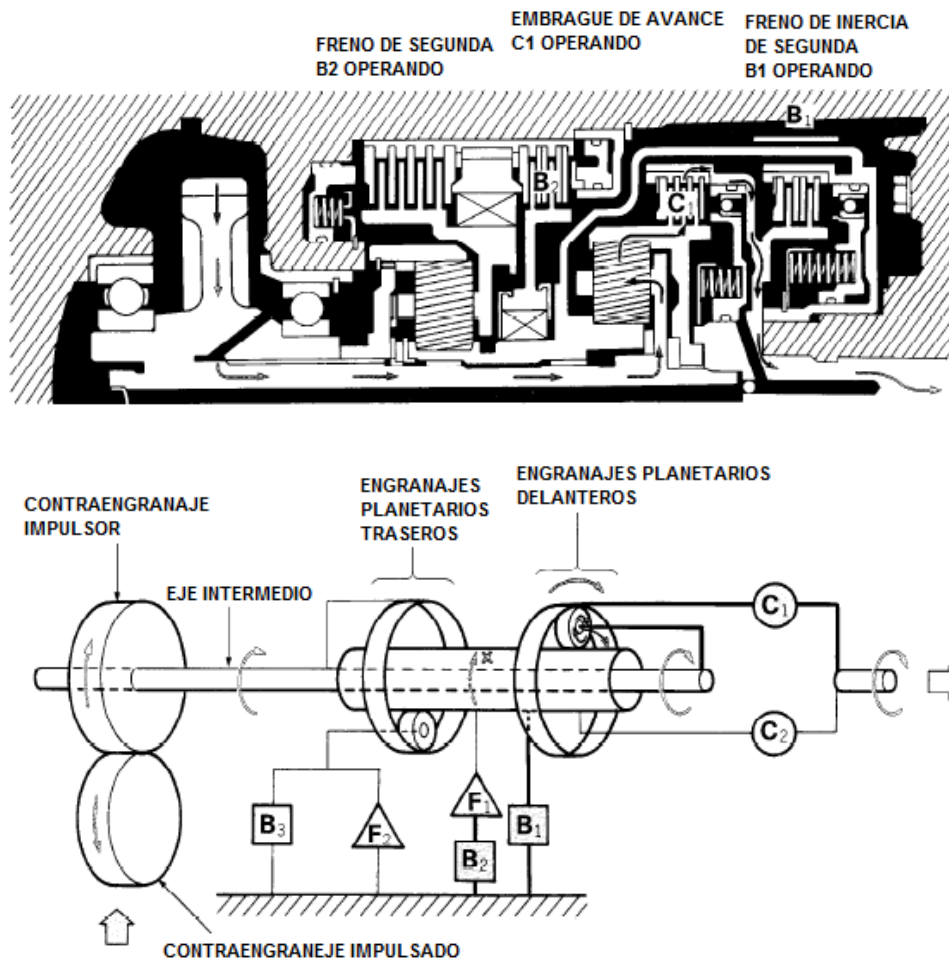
Transmisión en rango “2”. Engranaje de segunda.
